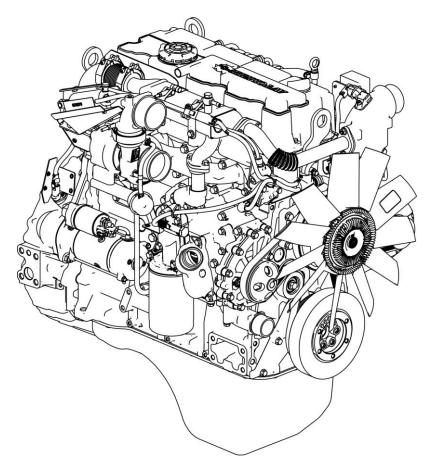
Двигатель ЯМЗ-53443-30 (общий вид справа)
